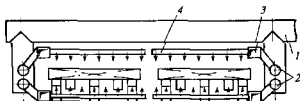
Схема печи струйного нагрева алюминиевых слывов
